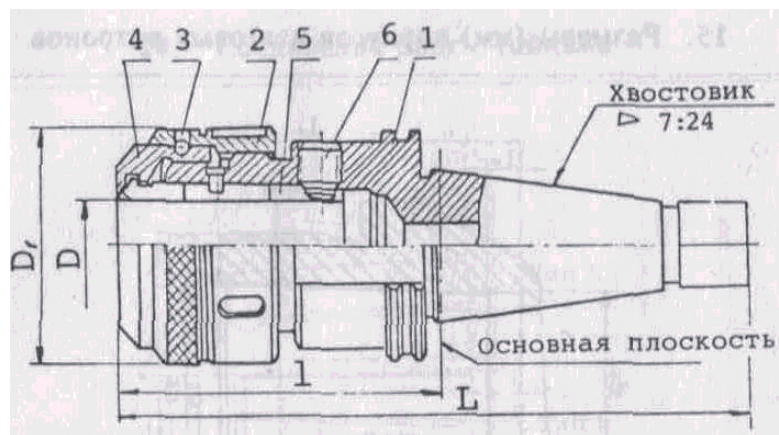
Цанговый патрон для быстрой замены режущего инструмента
